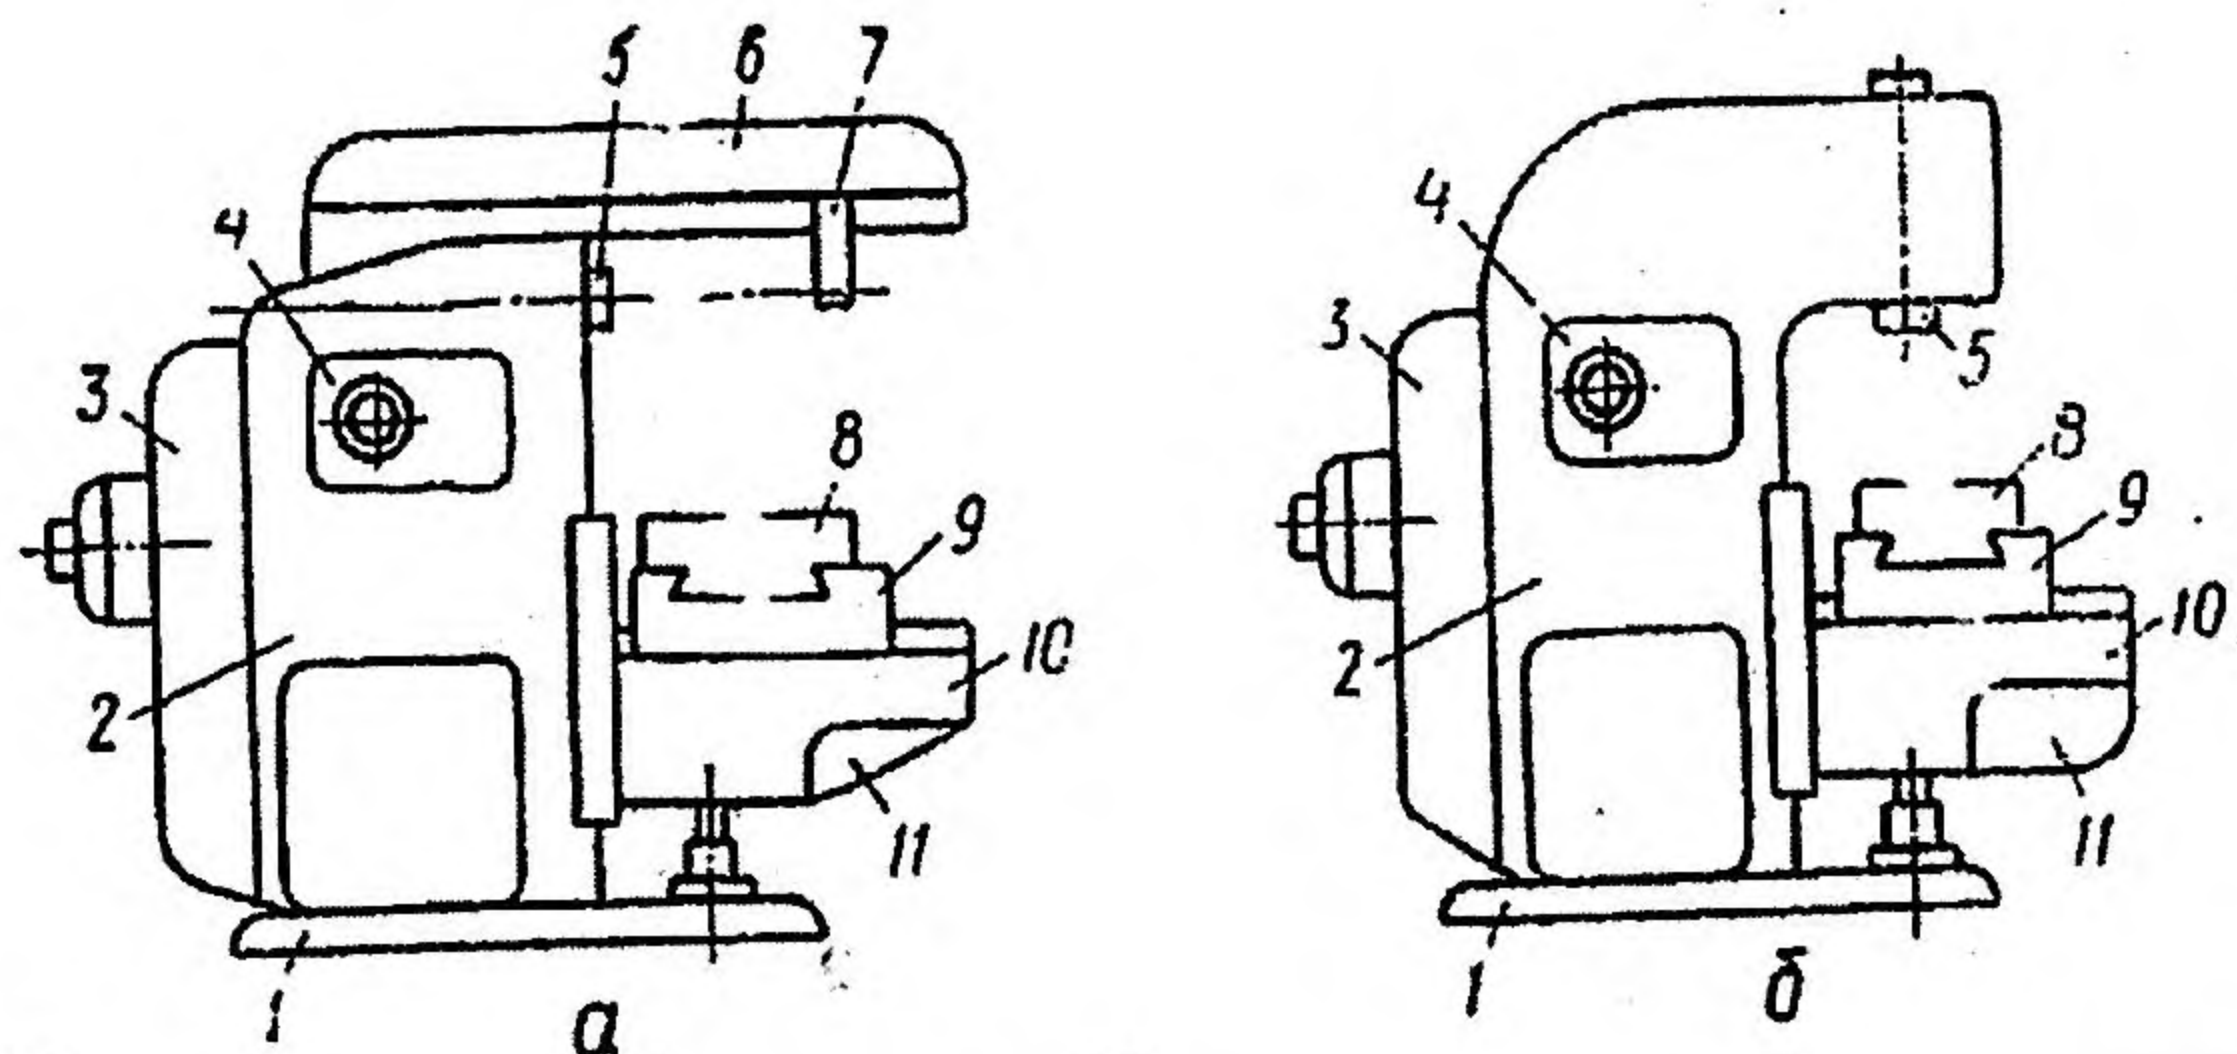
Горизонтально-фрезерный (а) и вертикально-фрезерный (б) станки
